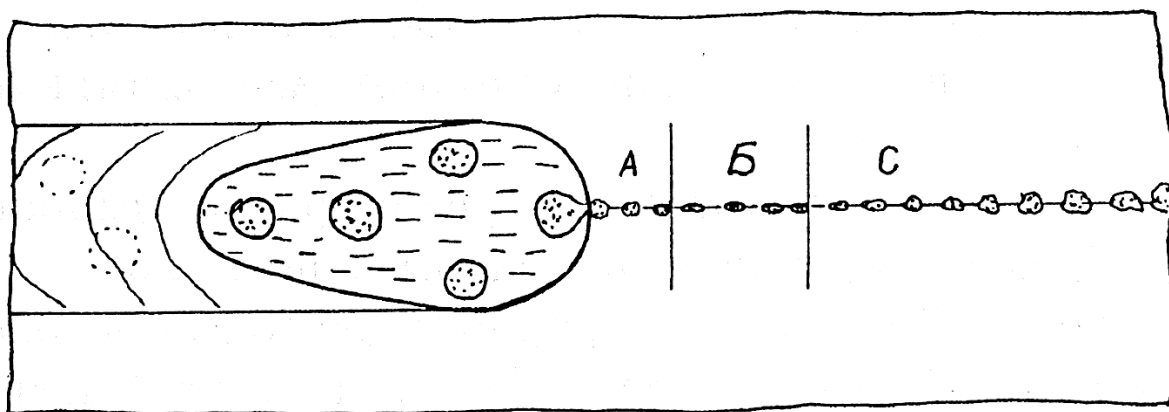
Схема образования закрытых полостей при сварке встык пластин алюминиевых сплавов [40]
